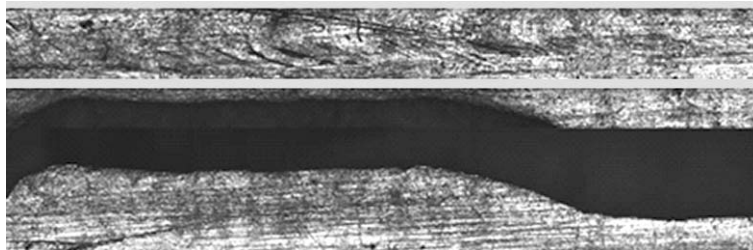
Характер разрушения сварного соединения при пластической деформации (вид сверху)
